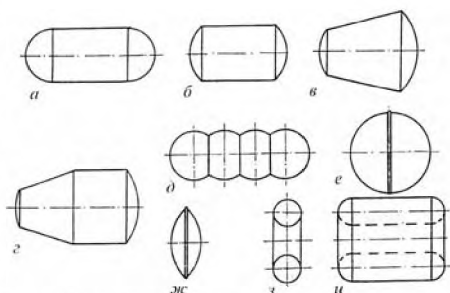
Формы баков: а, б – цилиндрические; в – конусные; г – сложной формы; д – ячеистый бак; е – сферический; ж – чечевичеобразный; з – торовый; и – кольцевой
